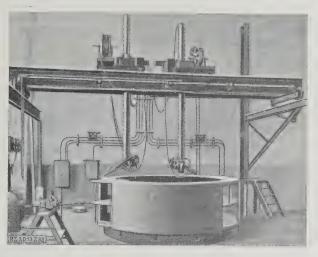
Schweißmaschine für Ständergehäuse; Außendurchmesser bis 4,25 m; kreisendes Gehäuse, stillstehende Schweißköpfe.
